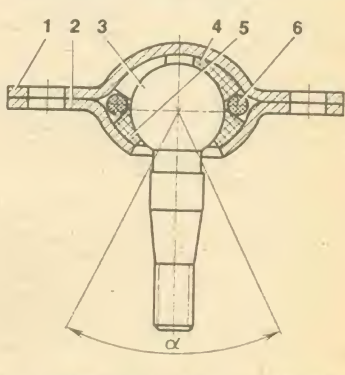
Шарнир ИЖ-2126-01: 1, 2 — верхняя и нижняя части штампованного корпуса; 3 — шаровой палец; 4, 5 — верхний и нижний антифрикционные вкладыши; 6 — компенсатор износа; α — угол качения пальца относительно корпуса.
